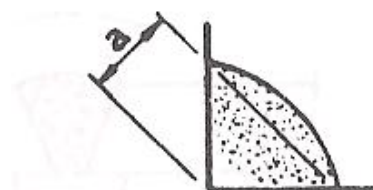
Pormenor do cordão de soldadura a realizar
